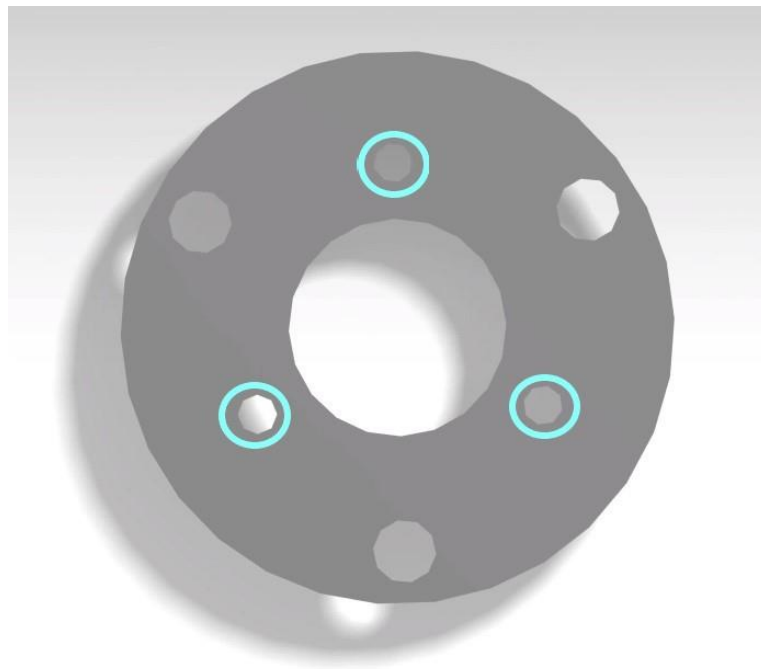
Vista en detalle del TALADRADO_1 de la tapa (Fuente: elaboración propia)
